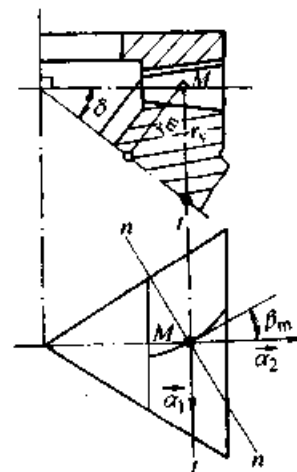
锥齿轮当量齿轮的端面和法面的选取
